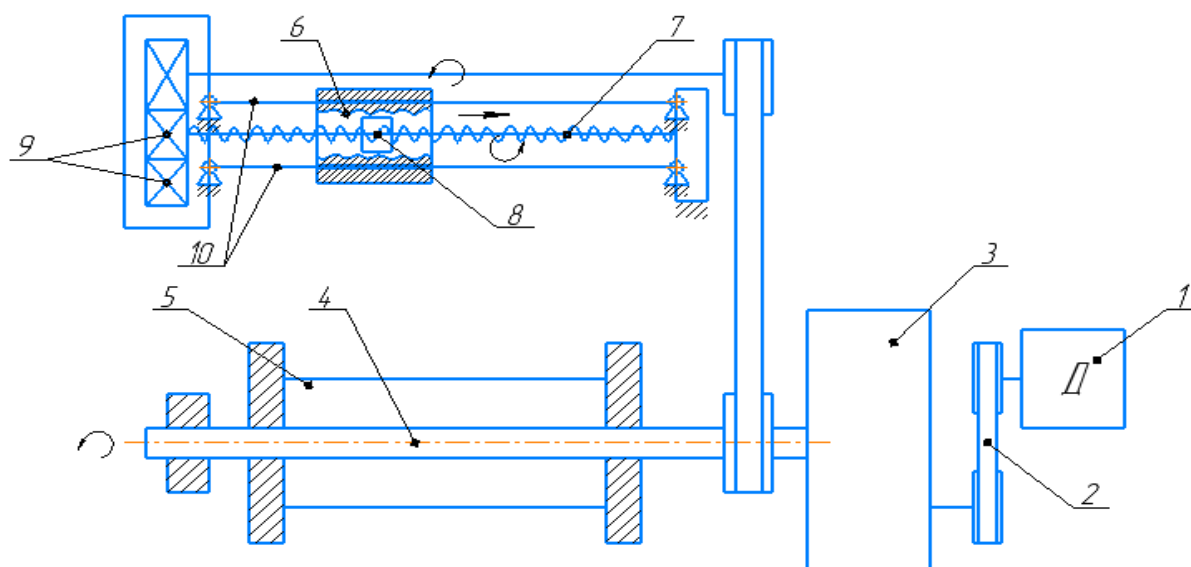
Кинематическая схема намоточного аппарата конструкции АЗТМ
